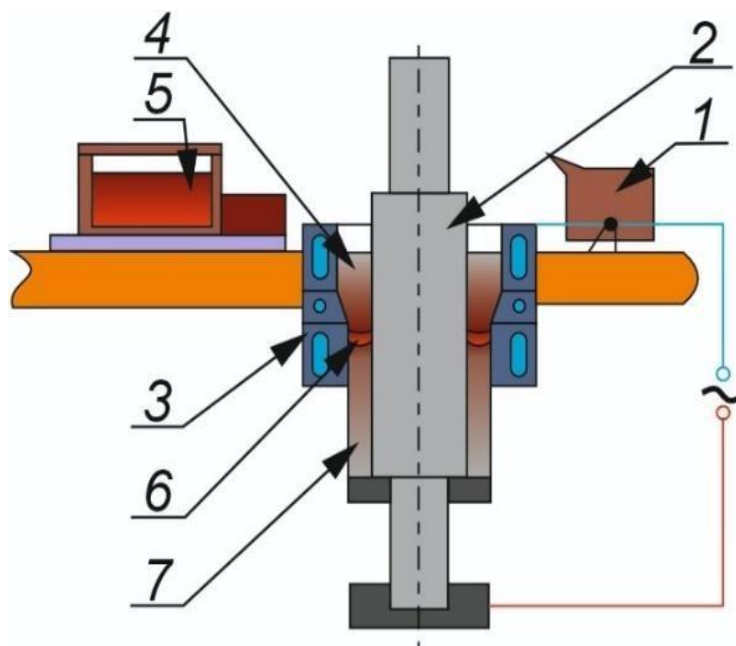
Схема процесу електрошлакового наплавлення рідким присадним металом у струмопідвідному кристалізаторі [73]: 1 – ківш для шлаку; 2 – виріб, що наплавляється; 3 – кристалізатор; 4 – шлакова ванна; 5 – дозатор рідкого металу; 6 – металева ванна; 7 – наплавлений метал
